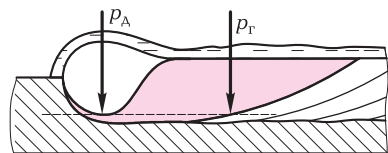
Расположение жидкого металла в головной и хвостовой частях сварочной ванны
